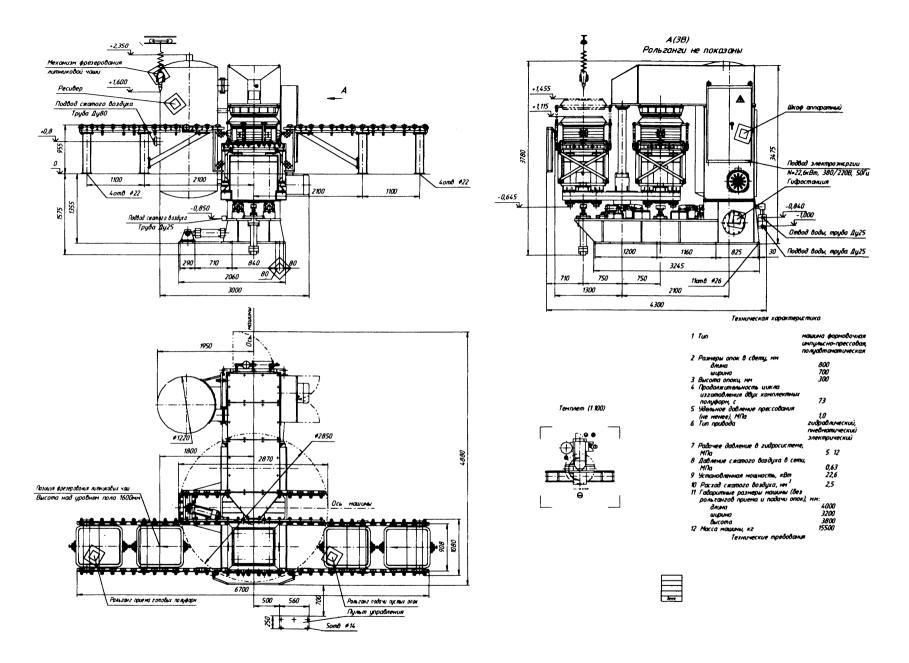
Габаритный чертеж формовочной машины мод. 4841
